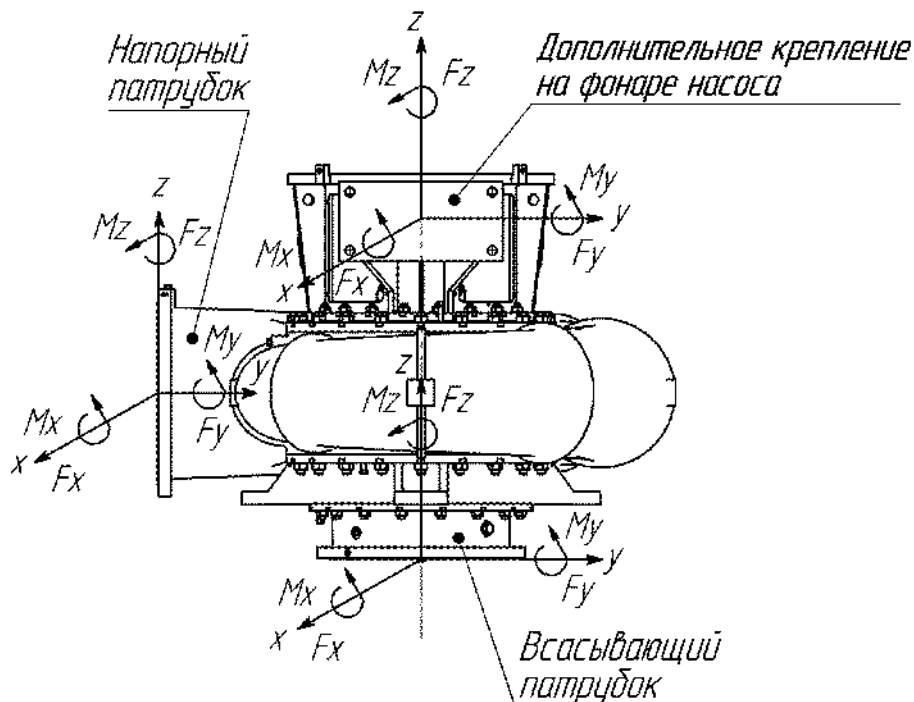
Допускаемые нагрузки на патрубки насоса из состава агрегата и дополнительное крепление
